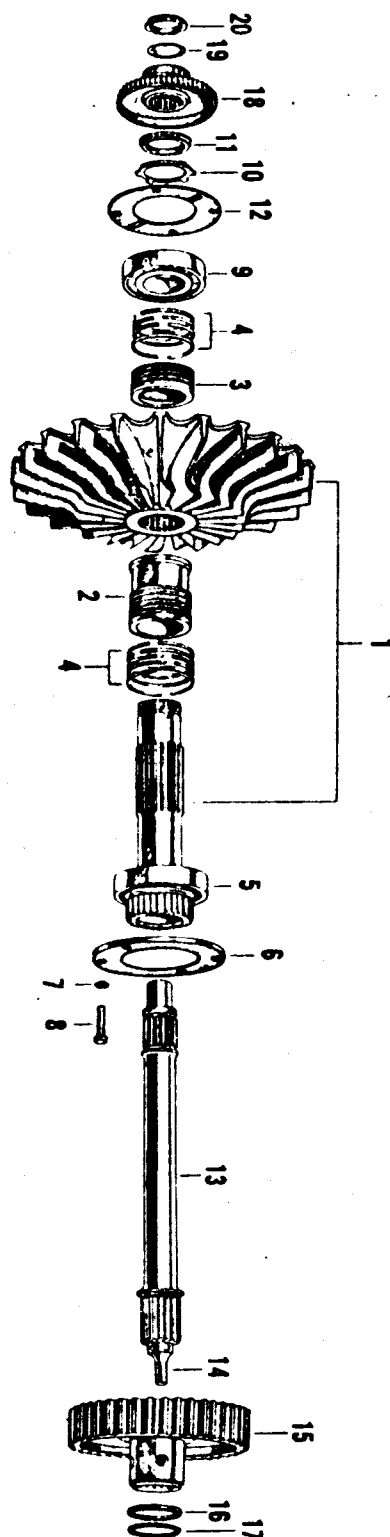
ROUE ET ARBRE DE COMPRESSEUR
